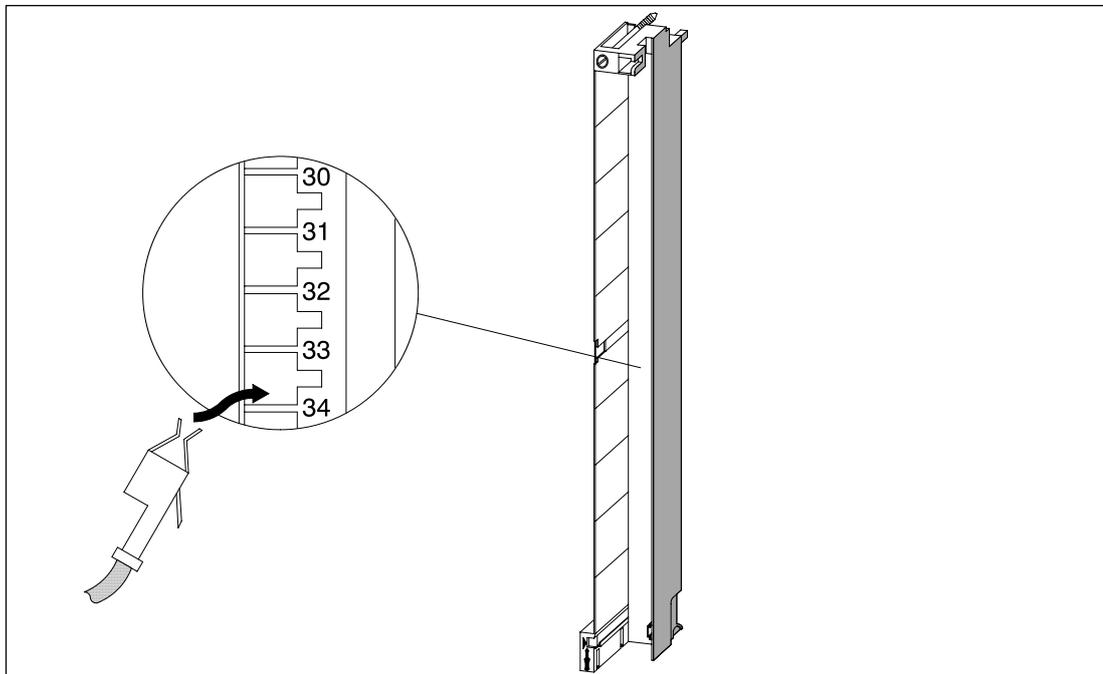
Cableado del conector frontal, terminales tipo pinza
